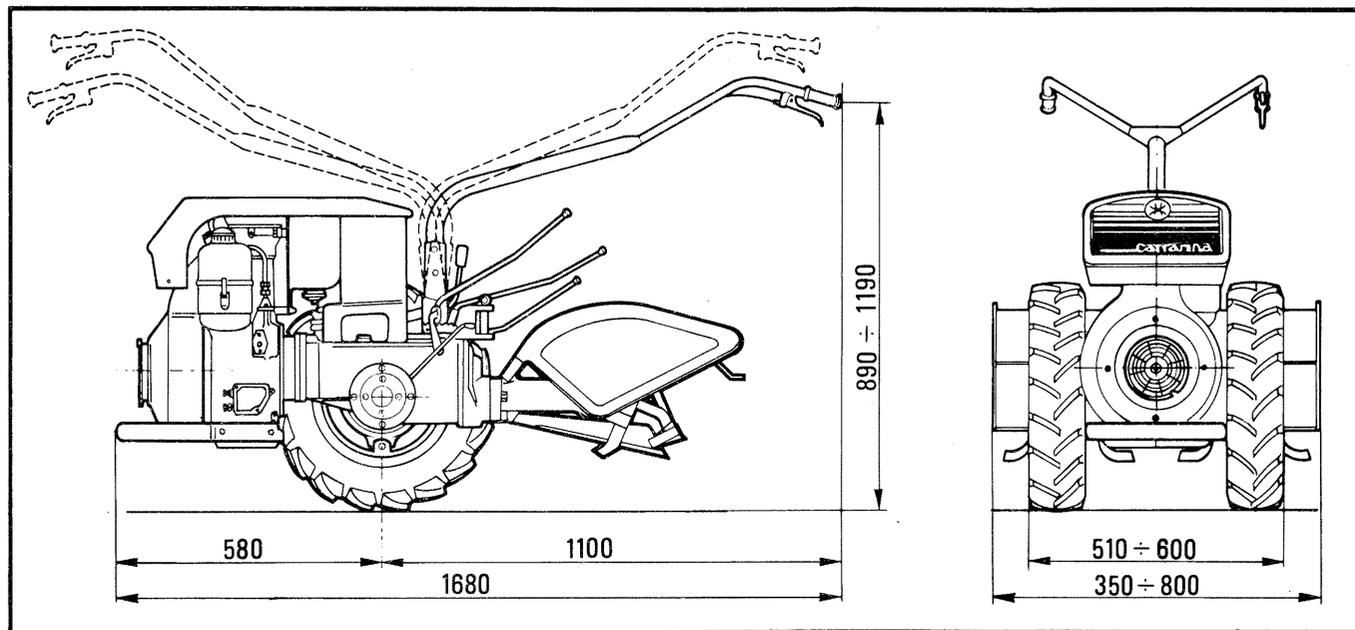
Dimensioni di ingombro Carrarina RV con pneumatici 4.00-10".
